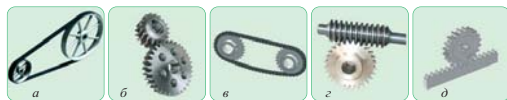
Передаточные механизмы: а – ременная передача; б – зубная передача; в – цепная передача; г – винтовая передача; д – зубчатоременная передача
